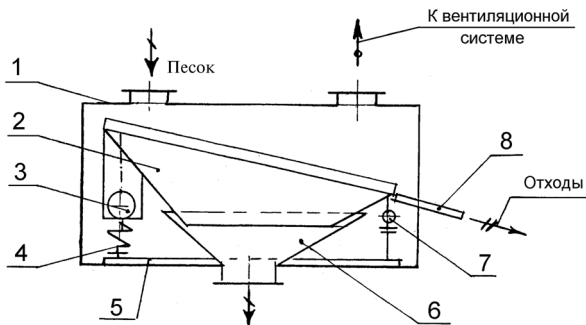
Вибросито: 1 - корпус; 2 - вибродека; 3 - электровибратор; 4 - эластичная опора; 5 - станина; 6 - воронка; 7 - шарнирная опора; 8 - лоток
